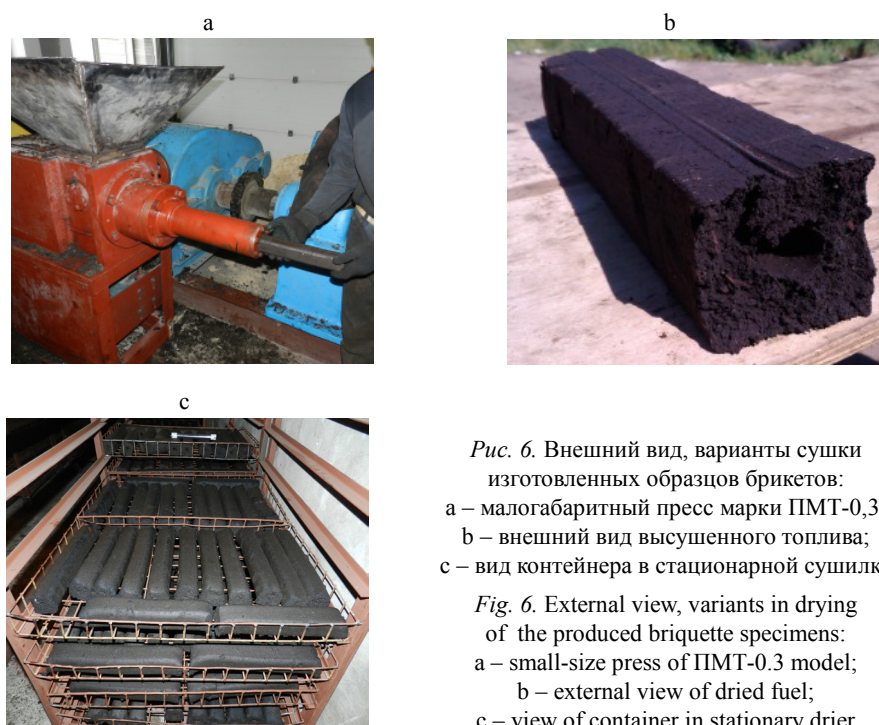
Внешний вид, варианты сушки изготовленных образцов брикетов:
